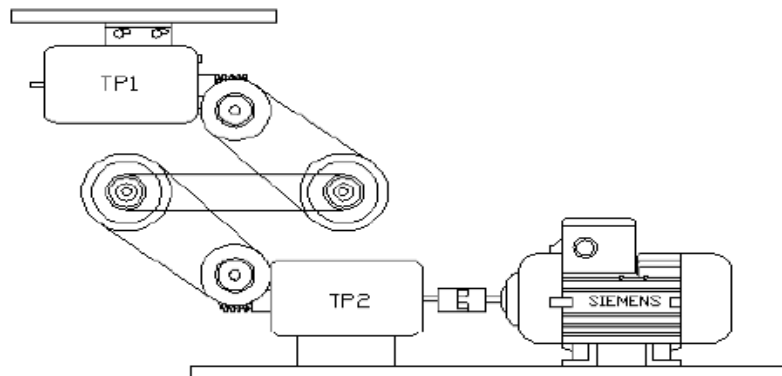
Sistema Mecánico de la máquina de ensayos universales MTS TK/T5002
